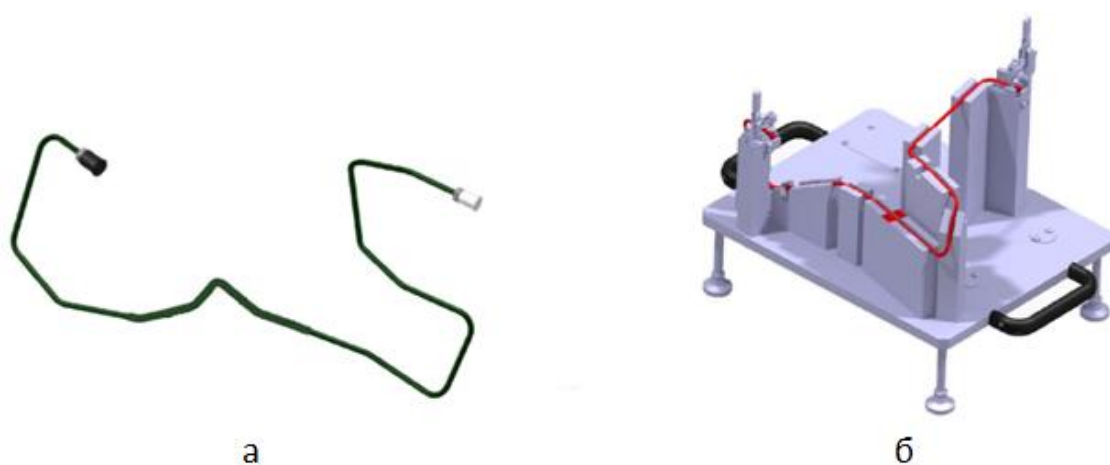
Контроль геометрии: а – тормозная трубка; б – специальный контрольный стенд
